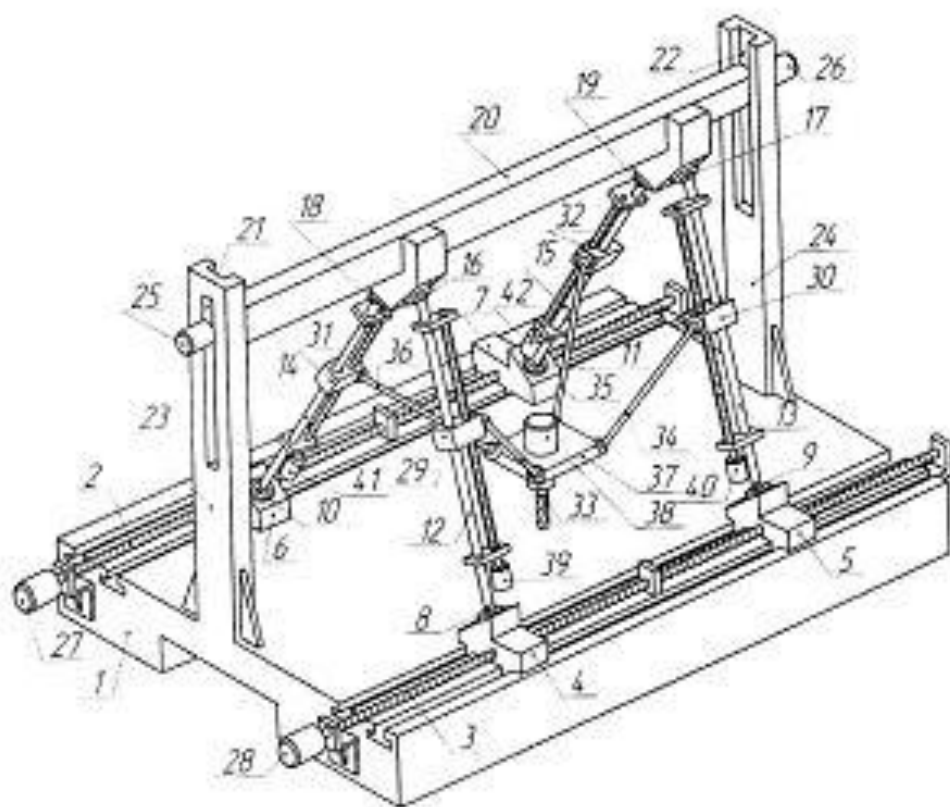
БАГАТООКООРДИНАТНИЙ ФРЕЗЕРНИЙ ВЕРСТАТ
